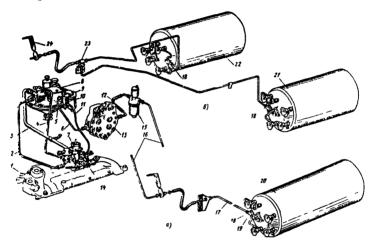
І Газовая топливная система автомобилей а — ЗИЛ-138; 6-ЗИЛ-138ВІ я ЗИЛ-138ІІ2; І-впускной коллектор;2-тру-бопровод от редуктора к смесителю системи колостого кода;3-трубопровод от редуктора к смесителю;4-шланг от редуктора к впускному трубопровод от редуктора к смесителю;4-шланг от редуктора к влектромагнителому клапану пусковой системи;6-трубопровод от испарителя к газового редуктор;7-газовый смеситель;8-газовый редуктор;9-фильтр газового редуктора;10-влектромагнитный клапан пусковой системи;11-трубопровод от клапана пусковой системи к смеситель;12-шланг высокого давления от электромагнитного клапана к испаритель;12-шланг высокого давления от электромагнитного клапана к испаритель;13-испаритель;14-каробратор резервной окотеми;15- электромагнитный клапан; 16-17 — трубопроводи;18-скоростной клапан;19-саллонный тройник;20-кроештейн
